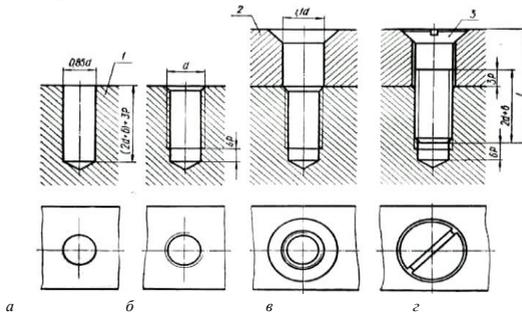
Послідовність викреслювання гвинтового з'єднання
